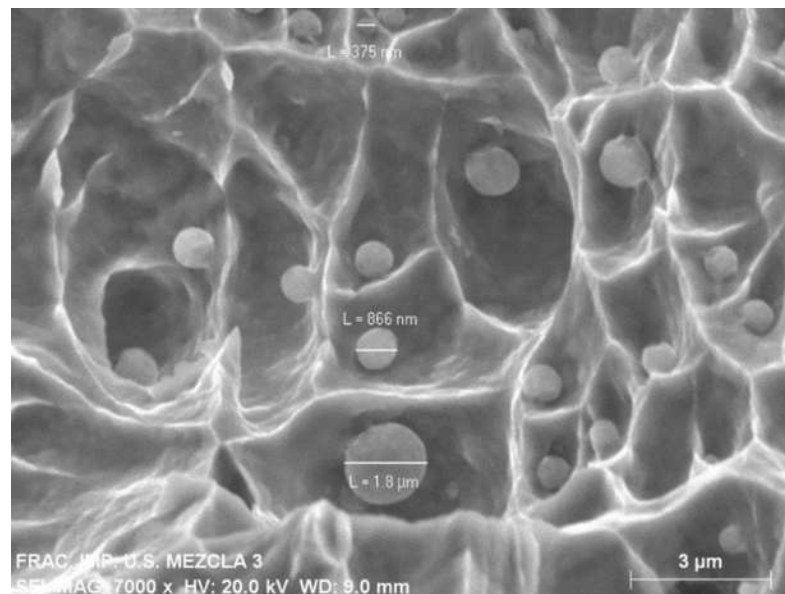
Tamaño de inclusiones en la unión soldada con 75% Ar – 25% CO₂.
